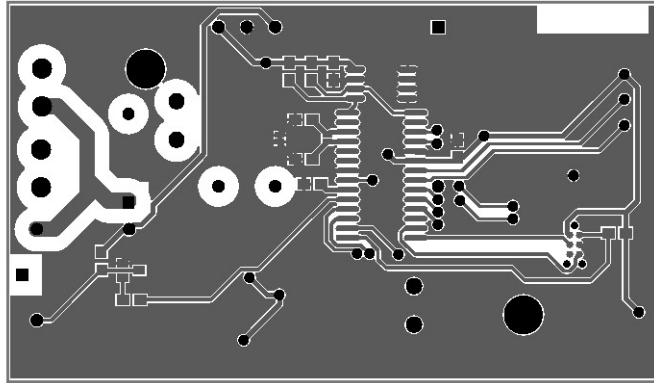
PCB cara BOTTOM (Escala 1:1)
